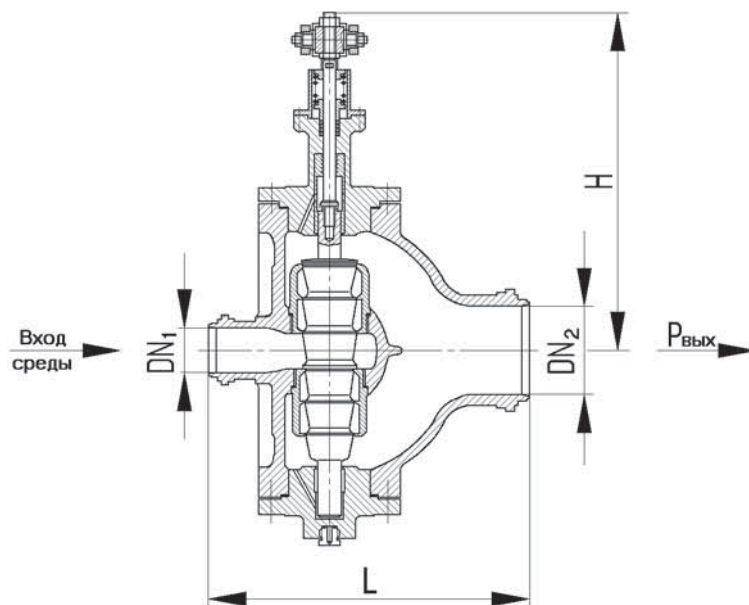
Клапан регулирующий проходной с патрубками под приварку с гидроприводом
